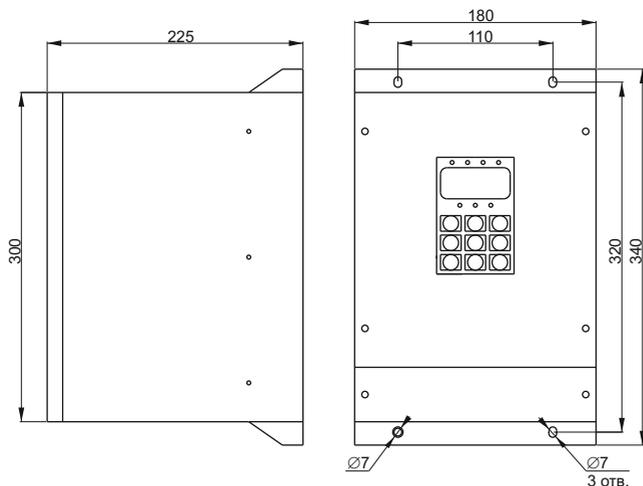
Габаритные и установочные размеры тормозного модуля
